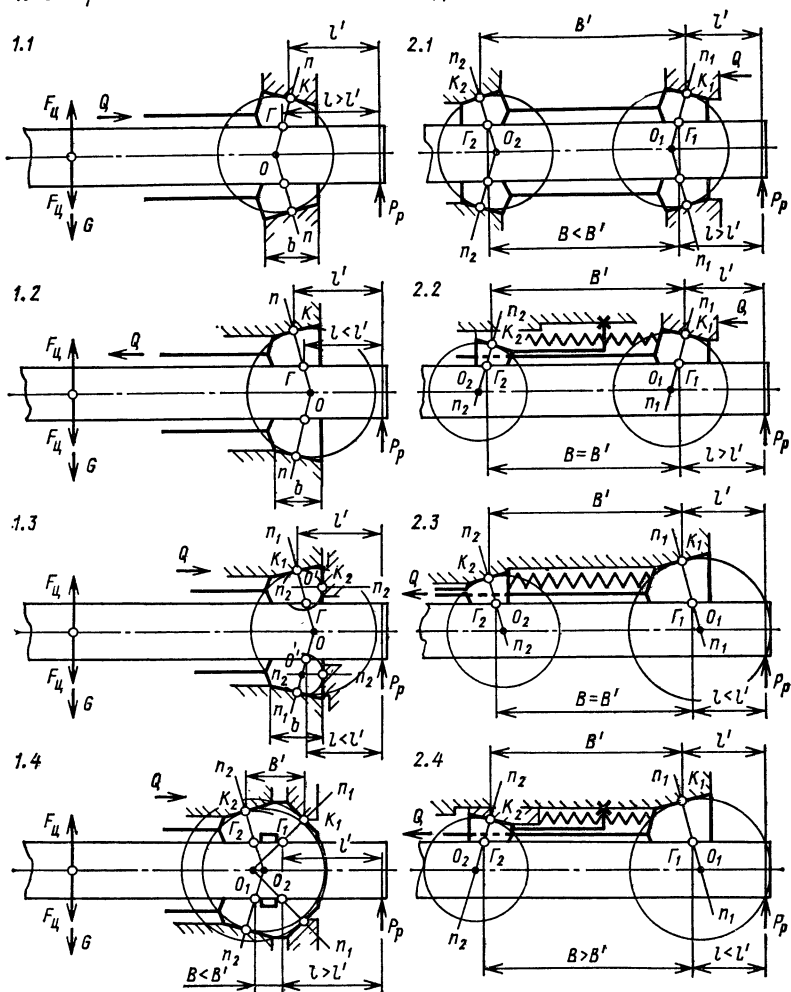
Схемы консольного закрепления в цанговых приспособлениях и патронах заготовок и хвостовиков режущих инструментов
